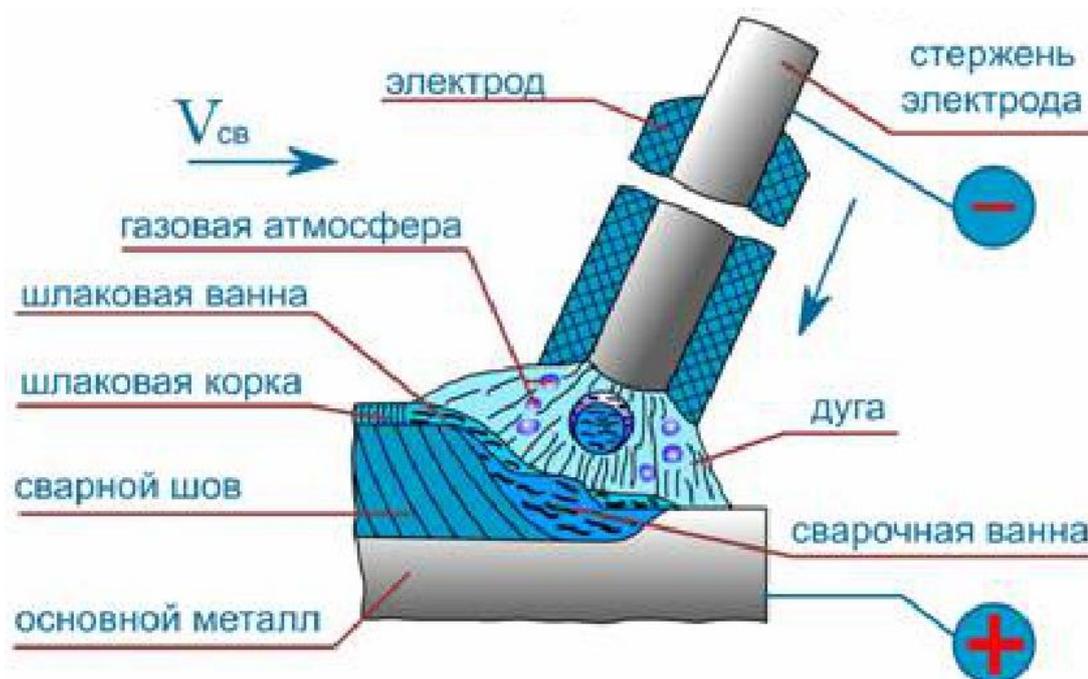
Схема выполнения ручной дуговой наплавки
